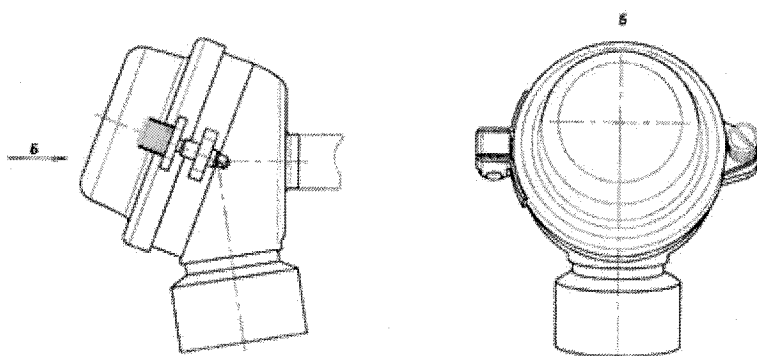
Кресленик зовнішньої частини ТСП-0690 (рис. 2) з головкою типу БАУИ.4087234.023 СБ
